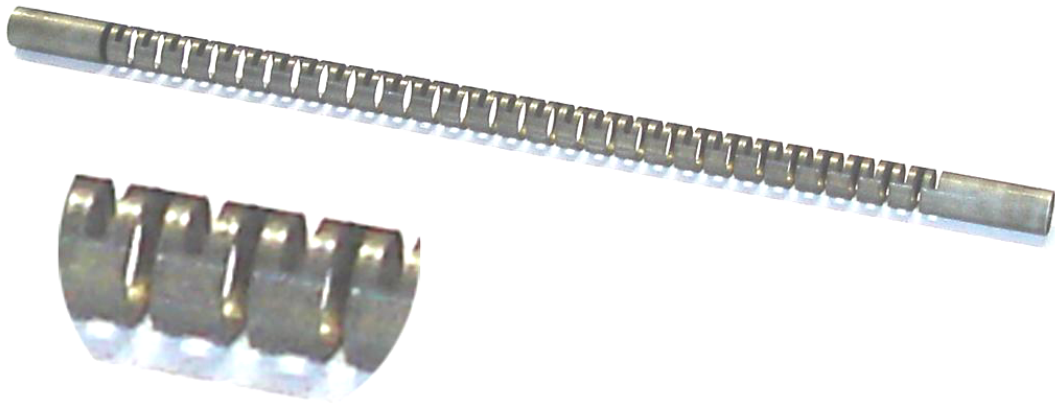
Fotografia e detalhe da estrutura de ondas lentas do tipo ring-bar caracterizada neste trabalho.
